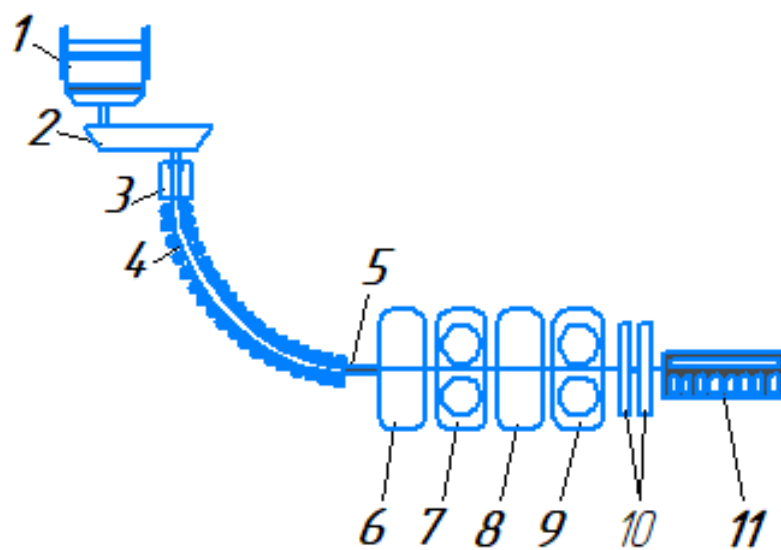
Компонування ливарно-прокатного модуля:
